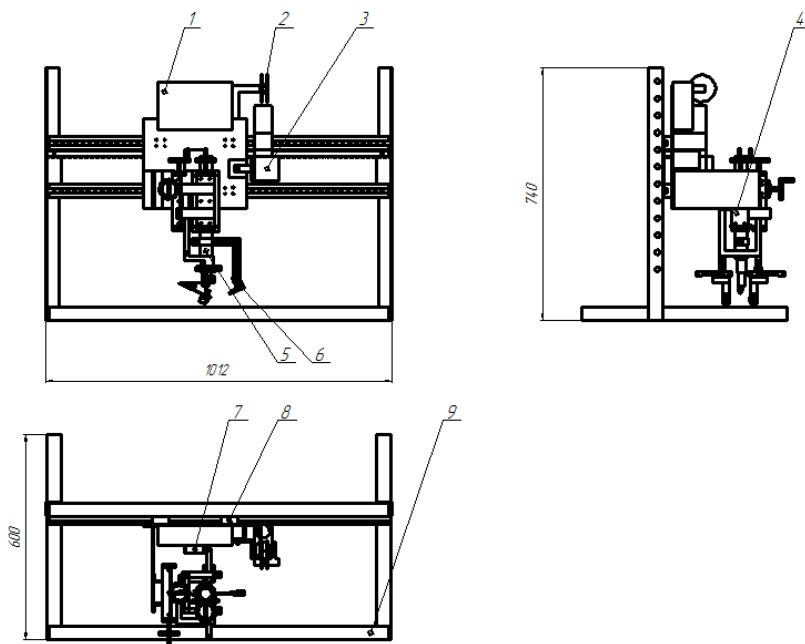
Габаритный чертёж комплектного портала с самоходной кареткой и сварочной головкой
